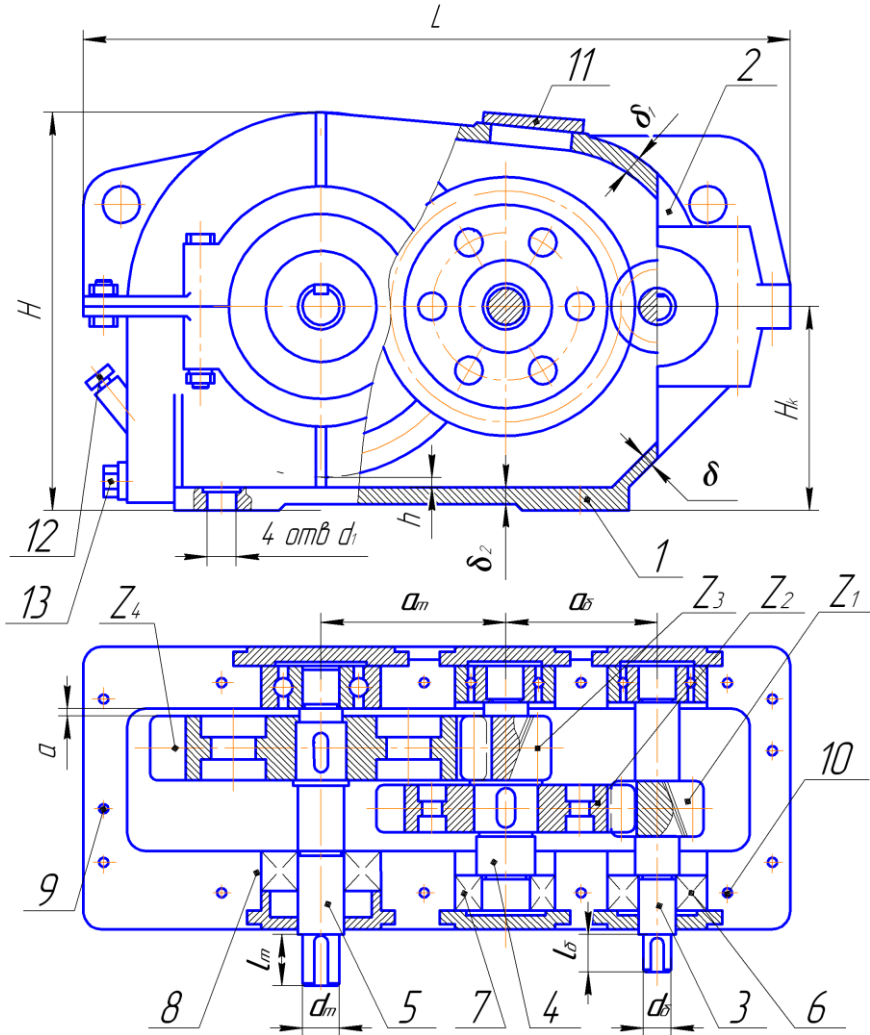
Редуктор двухступенчатый ЦДН-350
